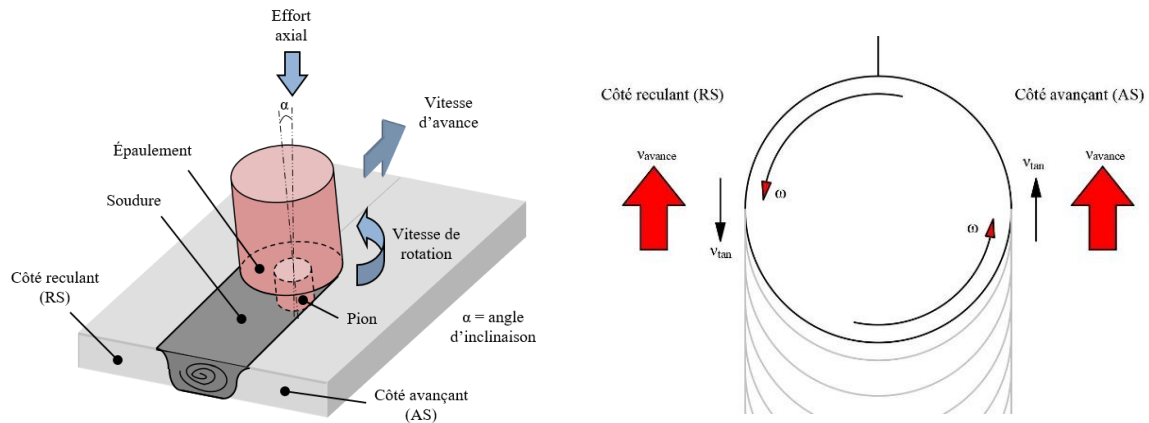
Représentation du soudage par friction malaxage
